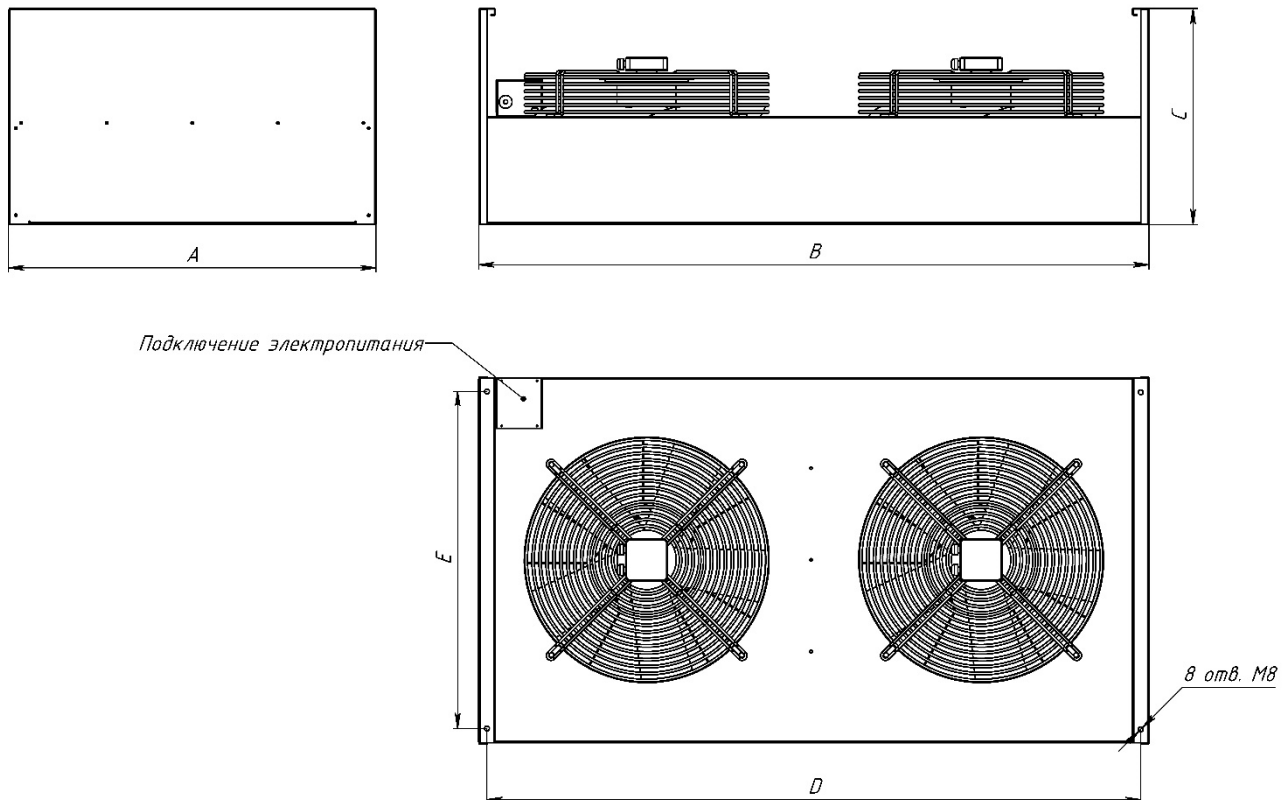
Габаритные и присоединительные размеры SA1 9400/20000/22500 D
